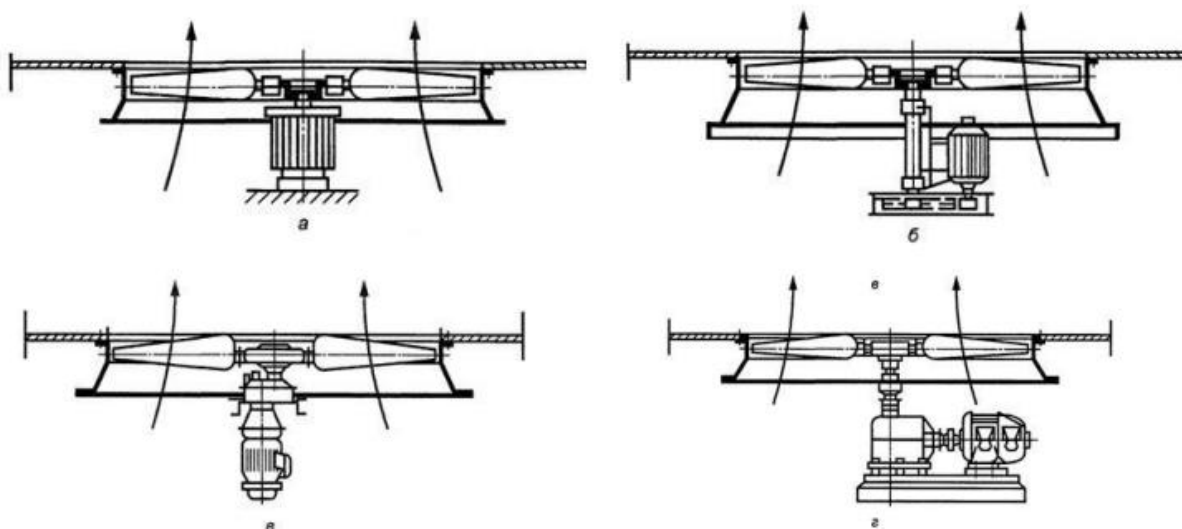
приводы аппаратов нагнетательного вида: а - непосредственный; б - клиноременный; в - редуктор с параллельными валами; г - редуктор с перпендикулярными валами
